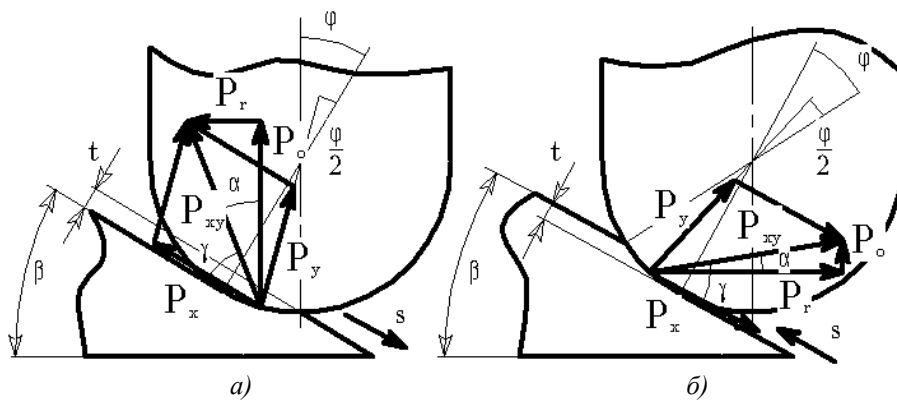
Векторна схема сил при фрезеруванні сферичною фрезою при $\beta < 45^\circ$:
